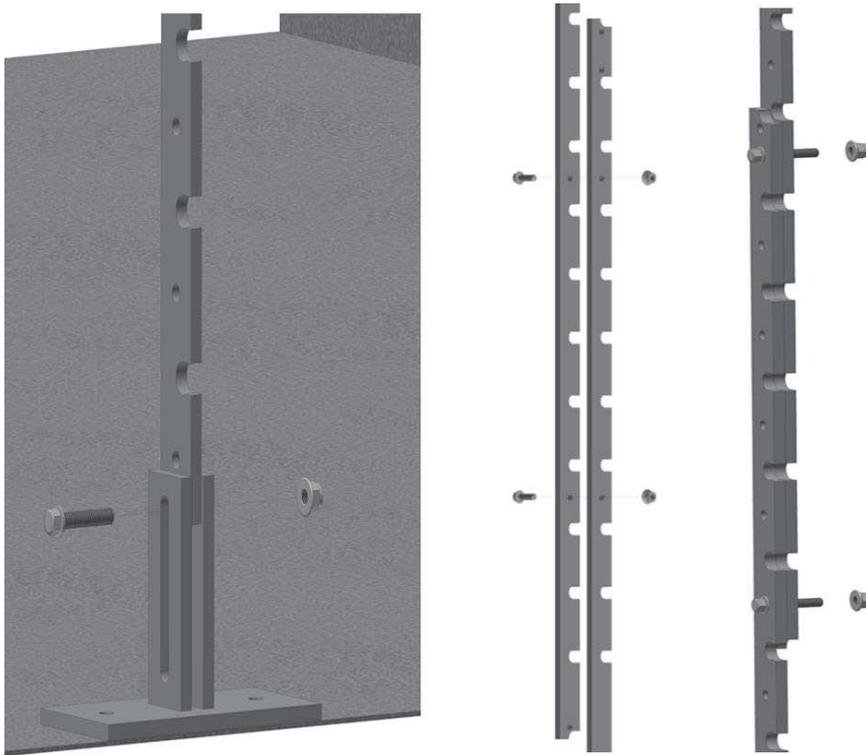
Installation du support inférieur sur la fixation de tuyau
